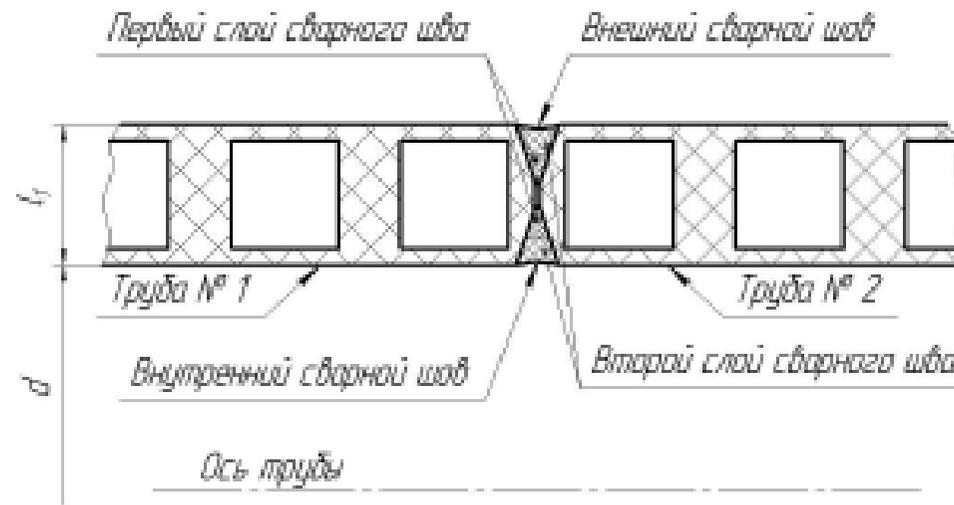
Конструкция сварного соединения при экструзионной сварке встык труб с проведением сварочных работ внутри и снаружи свариваемых труб
